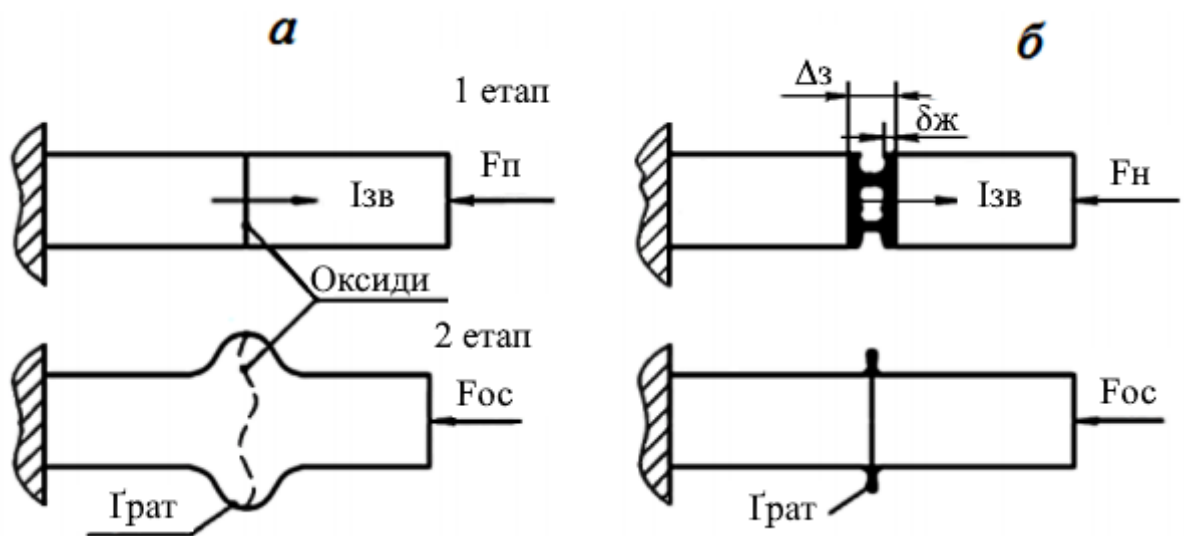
Етапи утворення з'єднань при стиковому зварюванні:
